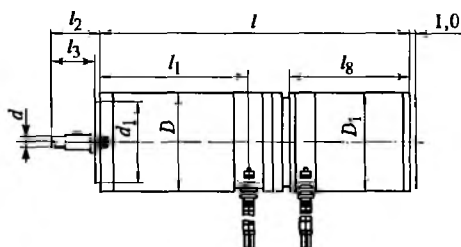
Габаритные и установочно-присоединительные размеры исполнительных коллекторных двигателей с полым якорем ДП35, ДП40, ДП50 и ДП60 исполнения по способу монтажа IM3681 (см. табл. 17.2)
